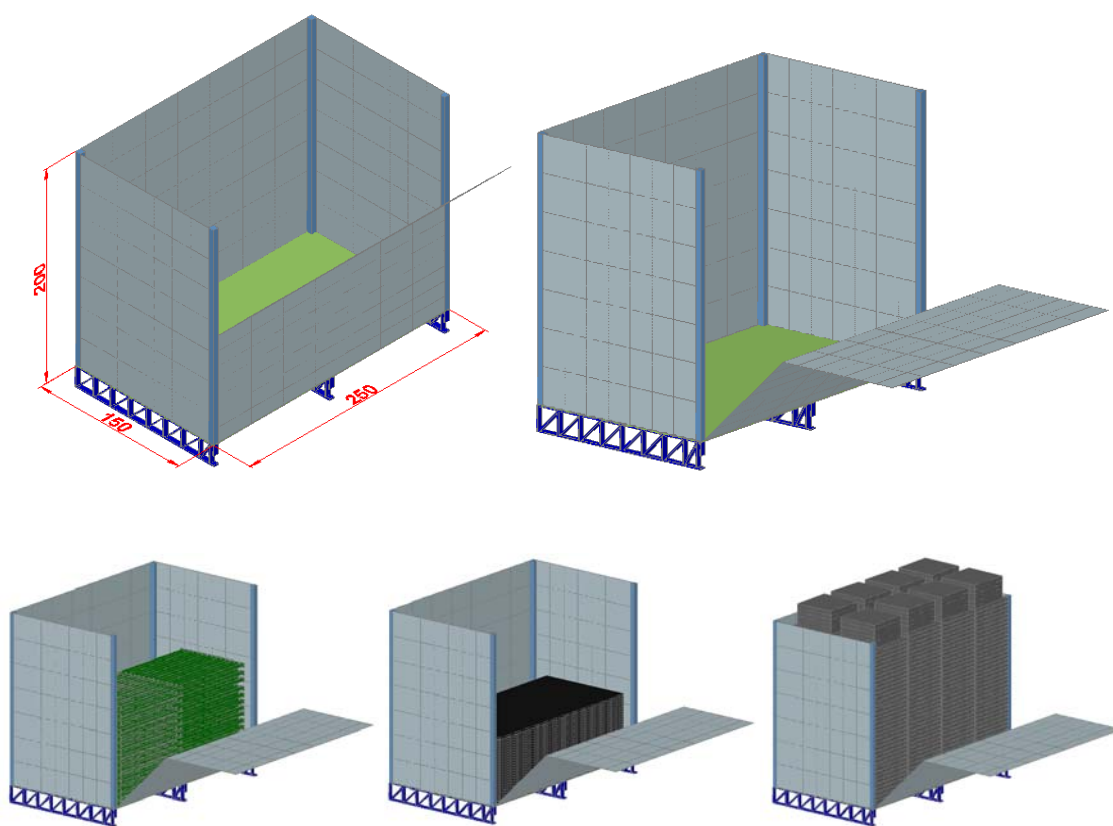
Caixa metálica utilizada no transporte de cubetas
